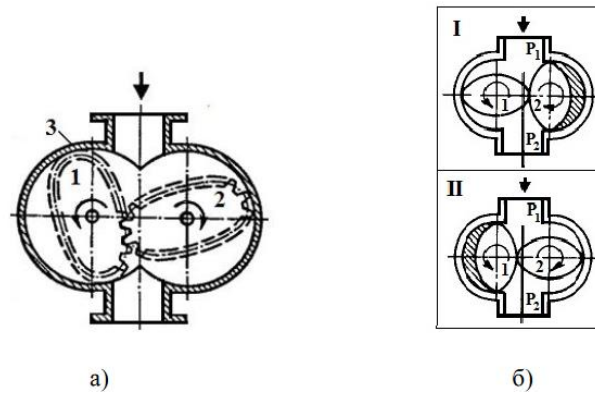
Схема витратоміра з овальними шестернями
